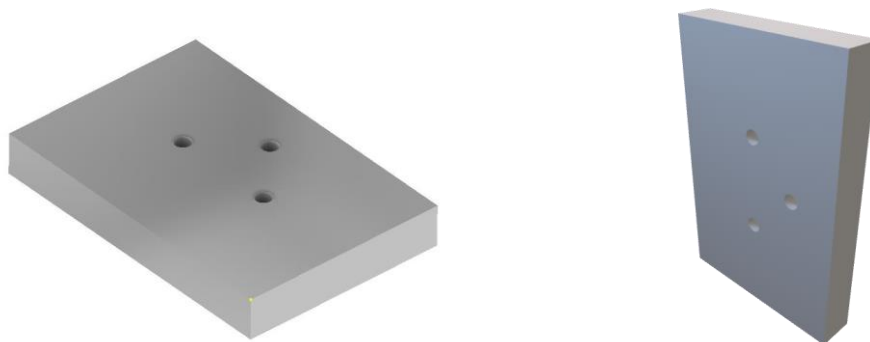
Τρισδιάστατη απεικόνιση αποστολής 45
